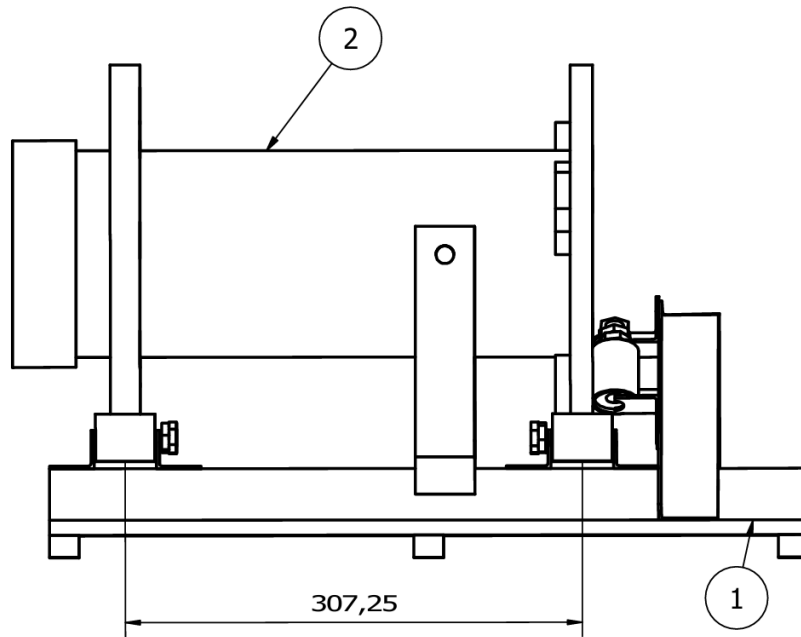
Rediseño de reactor montado en base de rodamientos.
